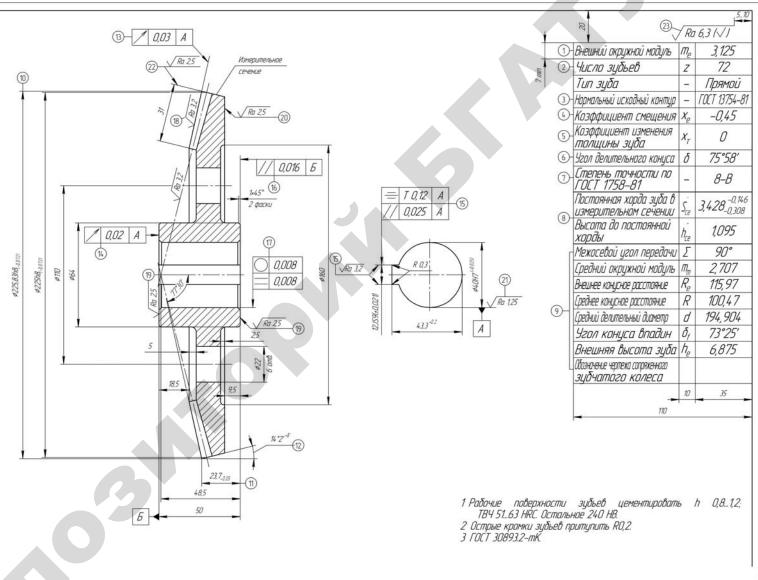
Схема простановки размеров и показателей точности для конического зубчатого колеса
